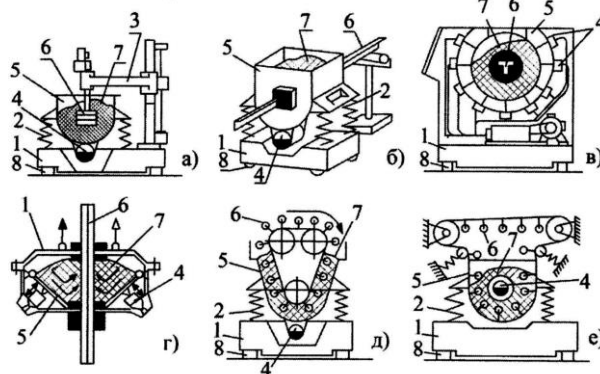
Схеми вібромашин прохідного та конвеєрного типу: 1 - основа; 2 - пружні елементи; 3 - рухома рама; 4 - вібратор; 5 - контейнер; 6 - оброблювана деталь; 7 - інструментальне середовище; 8 - амортизатори
